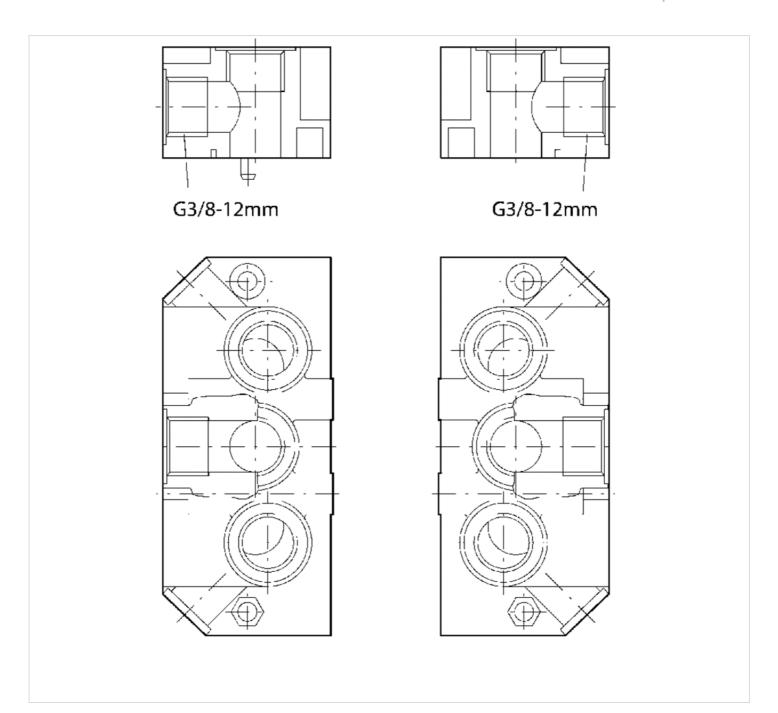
, Gewindeanschlüsse 1, 3 und 5 axial
